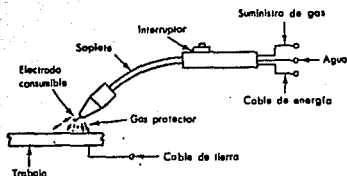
Equipo de portaelectrodo en la soldadura "MIG".
